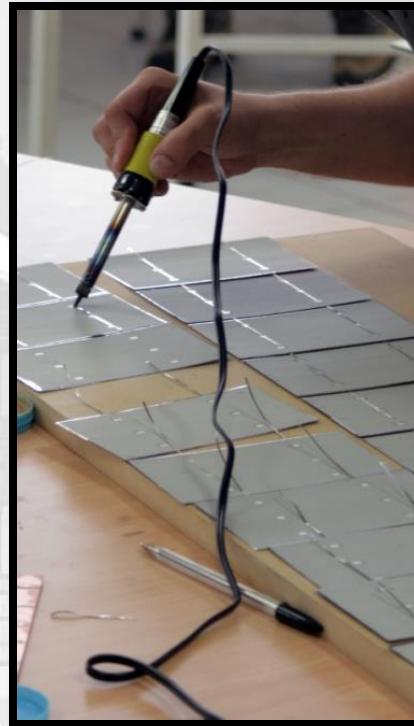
Ensamble y soldadura de Celdas Solares
